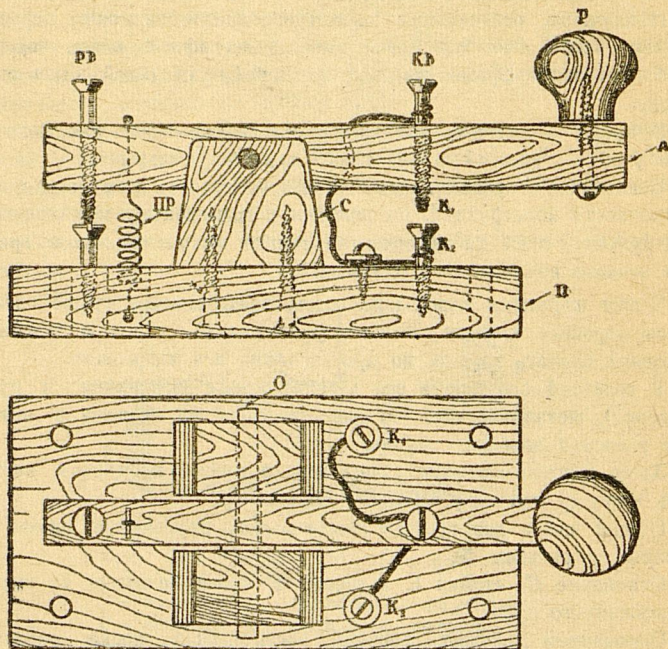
Самодельный деревянный телеграфный ключ: П — основание; С — стойка; А — рычаг ключа; Р — головка ключа; *K₁* и *K₂* — контакты; винты *K₁* и *K₂* (внизу) — клеммы для крепления проводов; ПР — пружина; КВ — контактный винт; РВ — регулировочный винт; О — ось.
